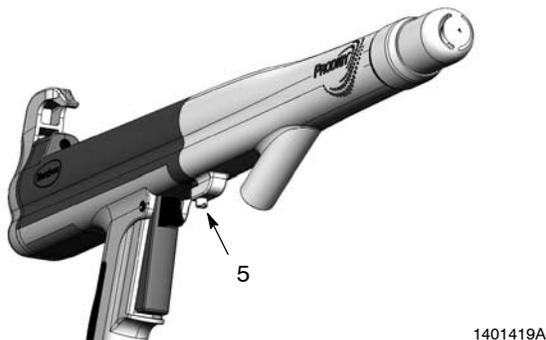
Desserrage de la vis de blocage de l'adaptateur
